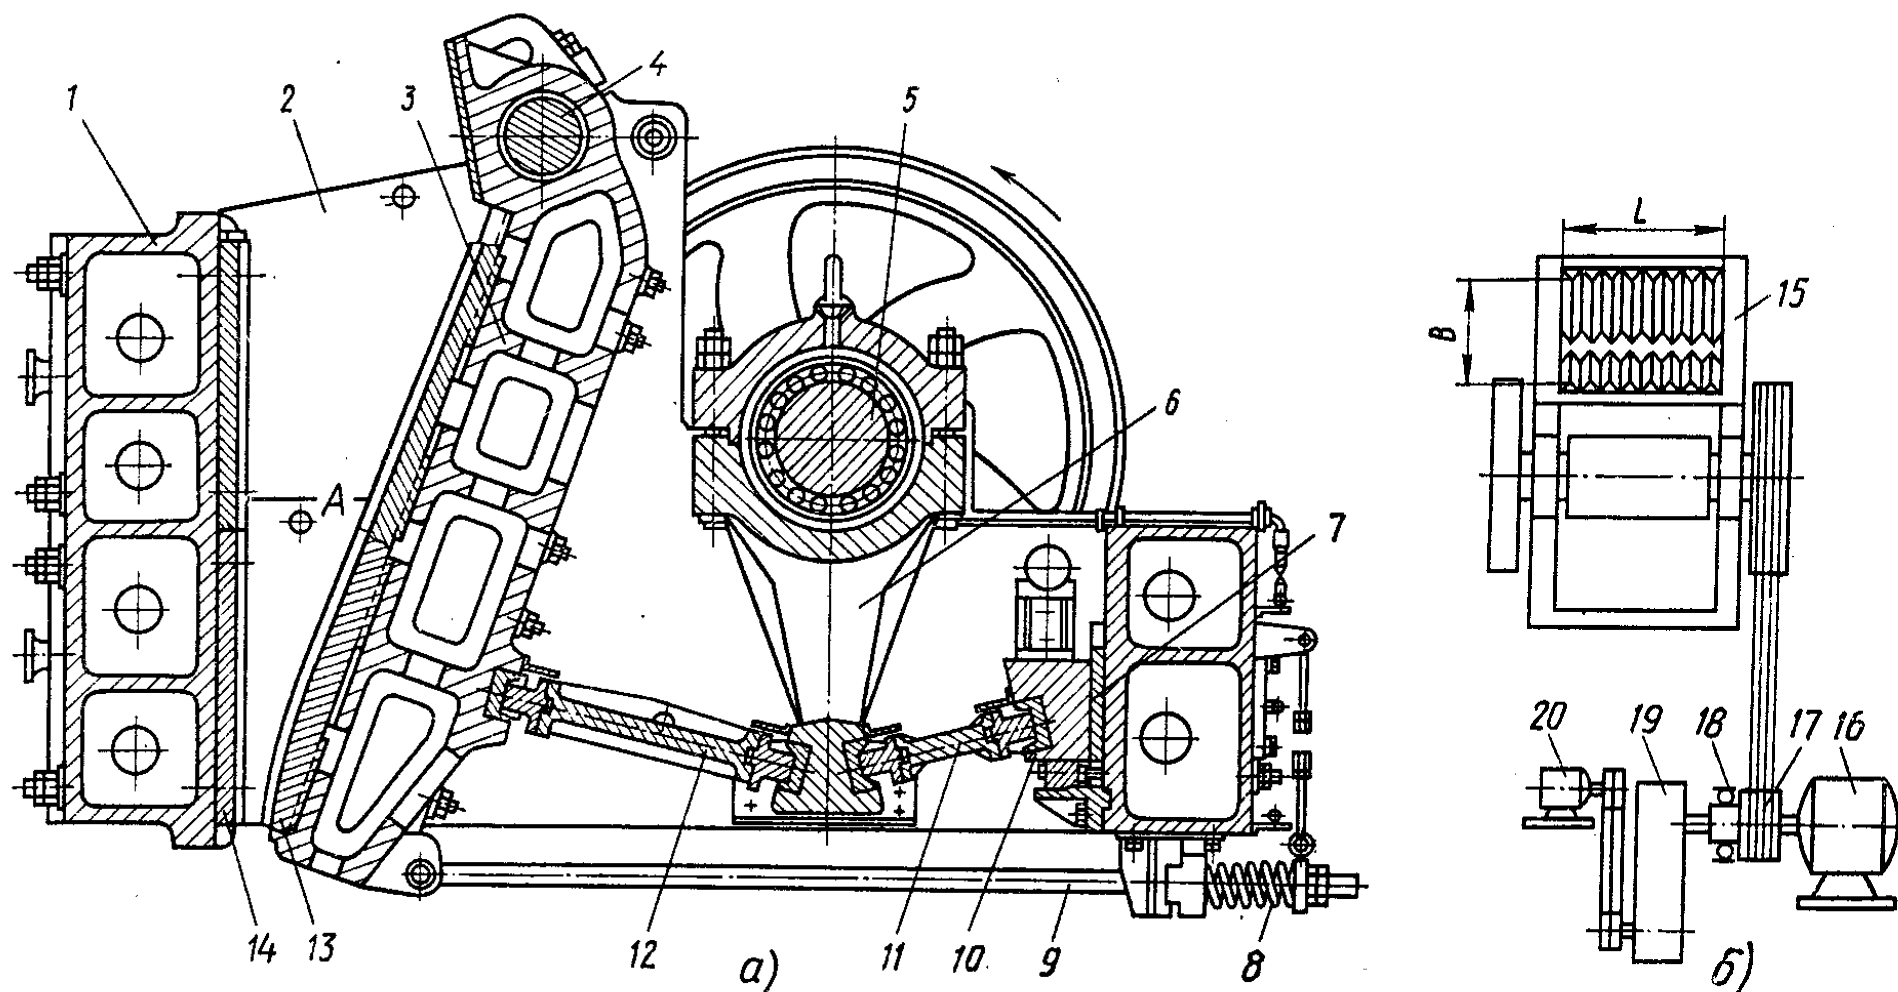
Щокова дробарка з простим рухом щоки: *а* – принципова схема; *б* – схема приводу;
